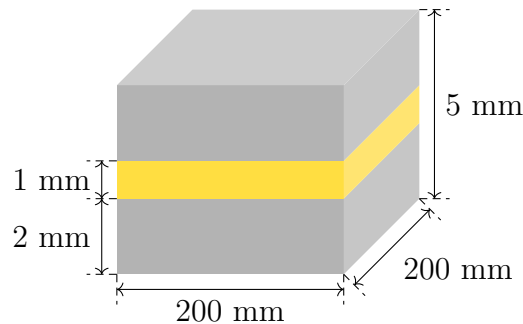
Dimensions d'un assemblage collé tri-couche.
